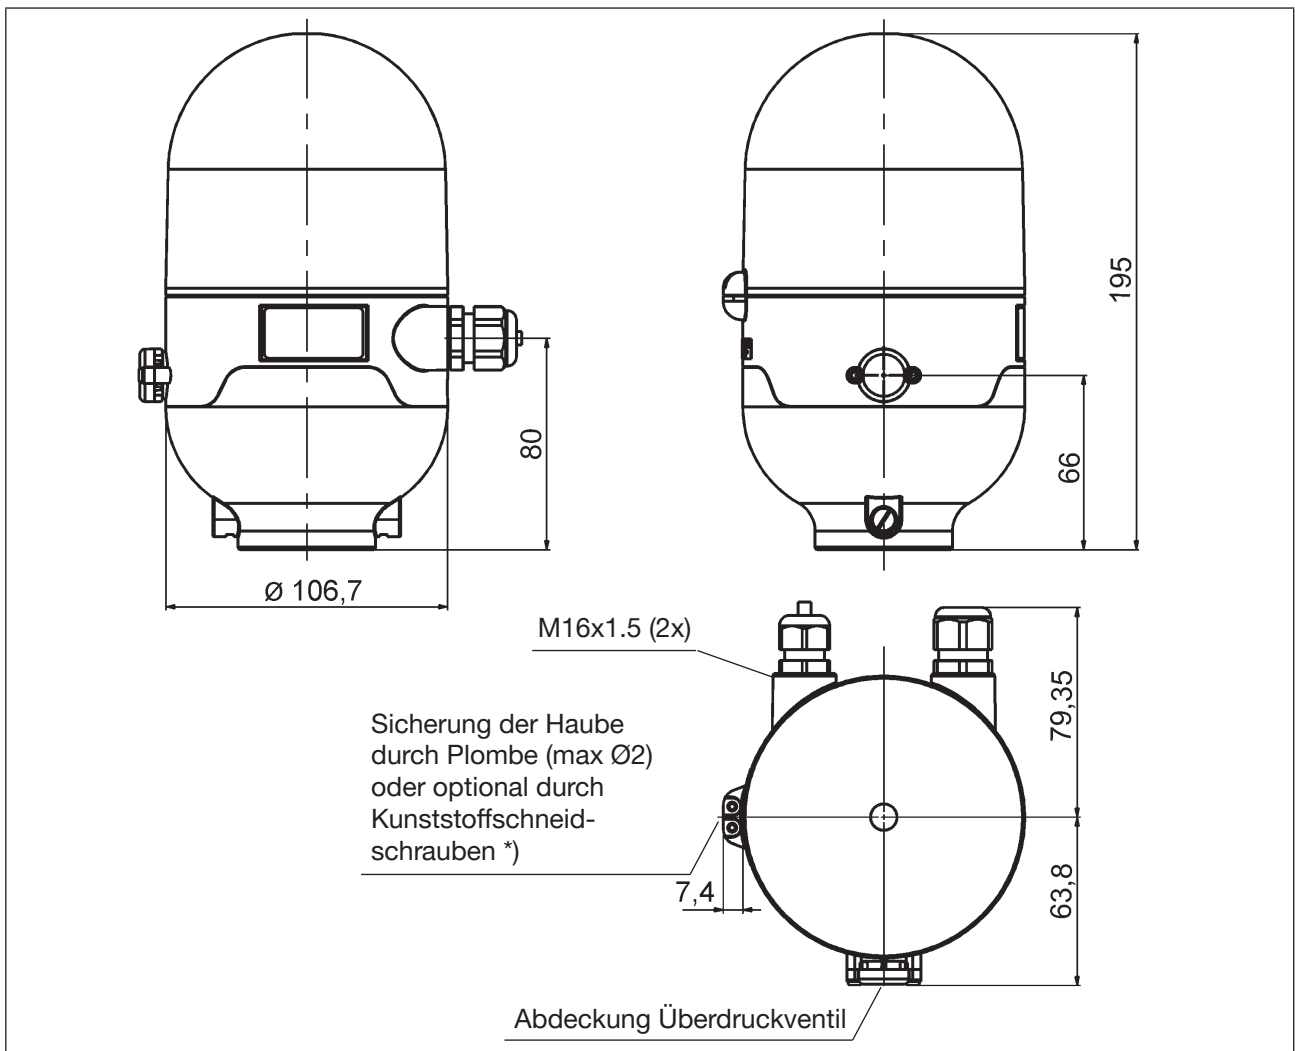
Maßzeichnung (für Varianten ohne Magnetventile)
